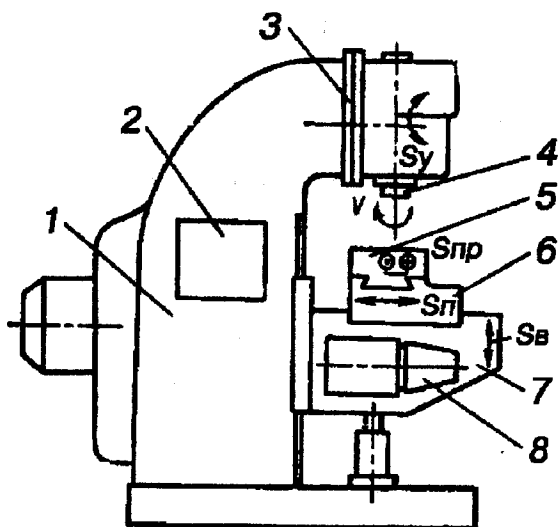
Загальний вигляд вертикально-фрезерного верстата
